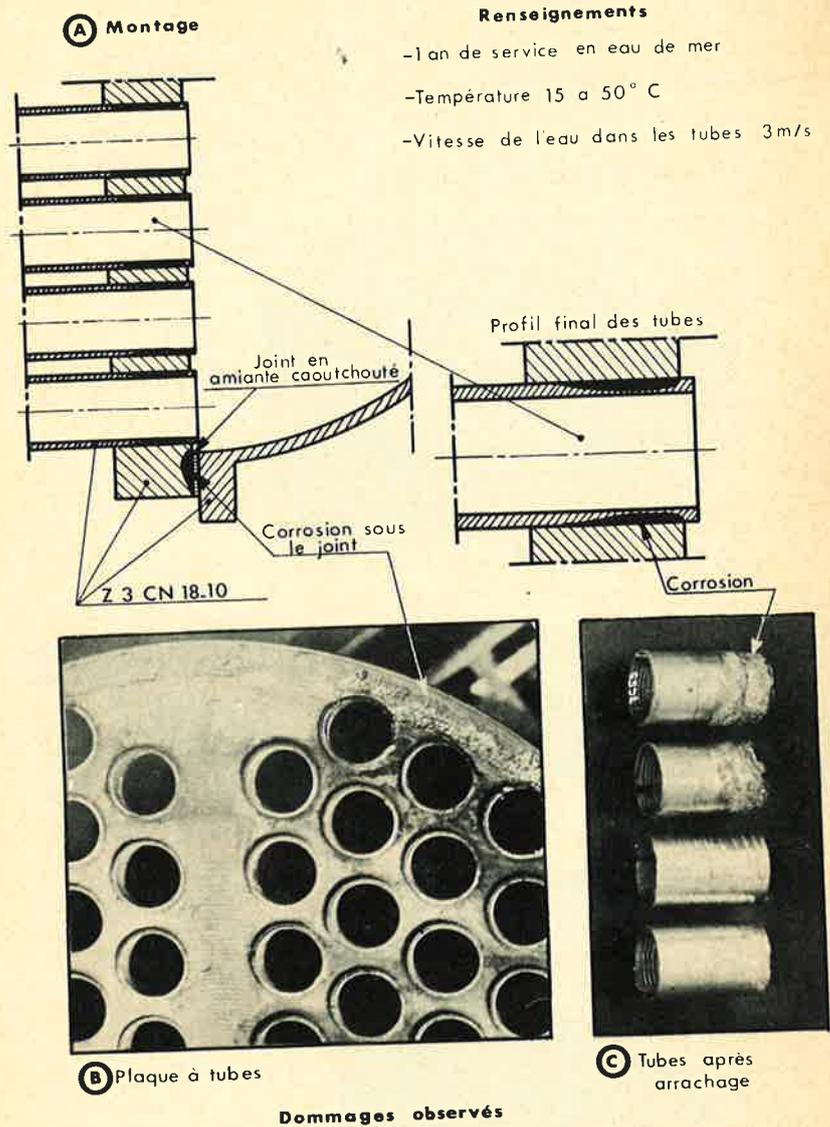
Plaque à tubes de réfrigérant d'huile
